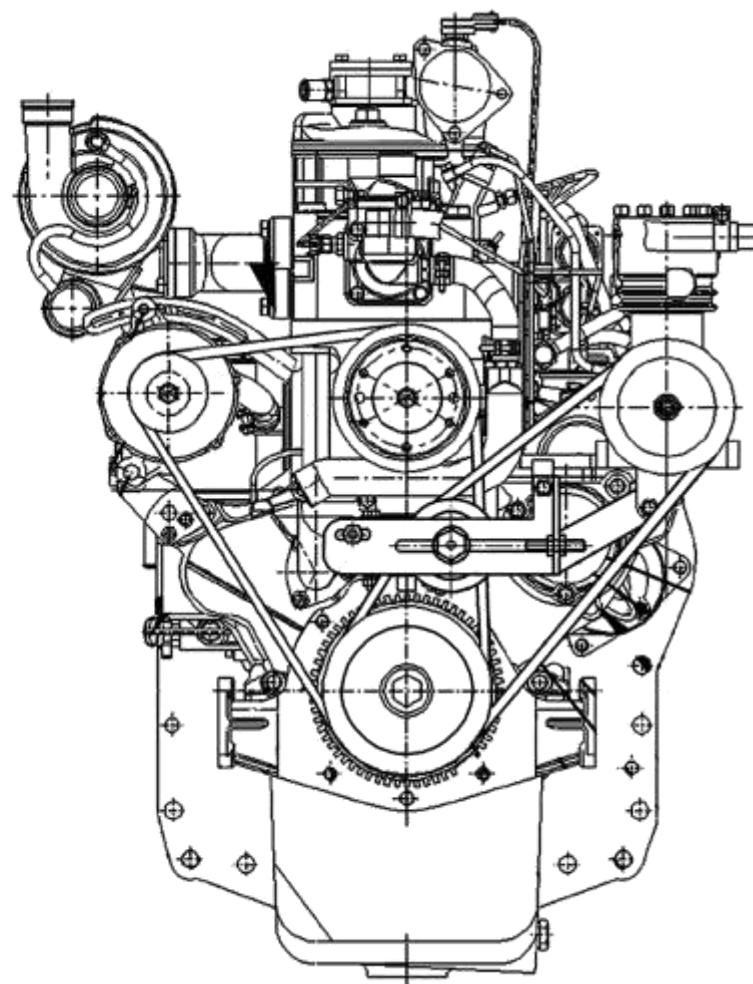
Общий вид дизеля Д-245.30Е3 с коробкой передач
